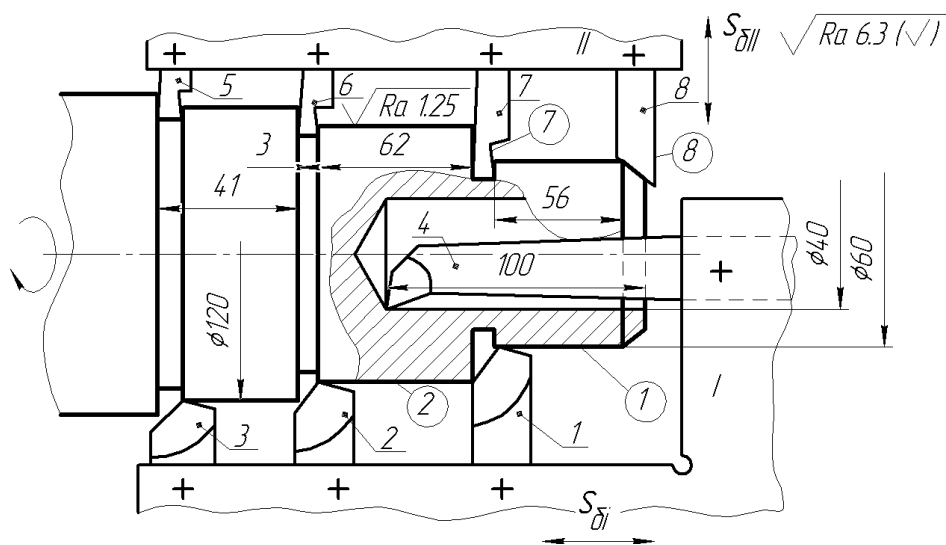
Схема багатоінструментального оброблення торця вала
